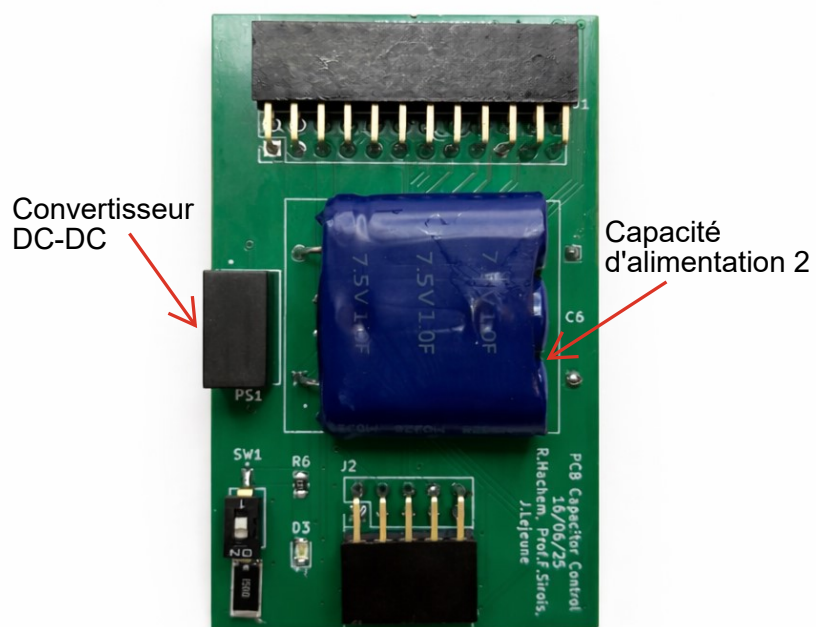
PCB de contrôle des capacités – vue face 2.
